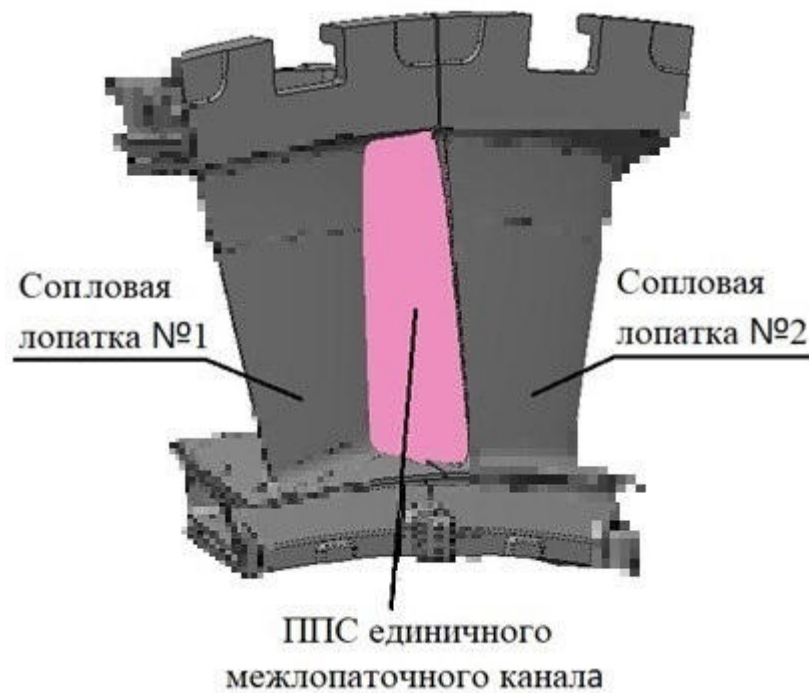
Схема расположения площади проходного сечения между двумя сопловыми лопатками
